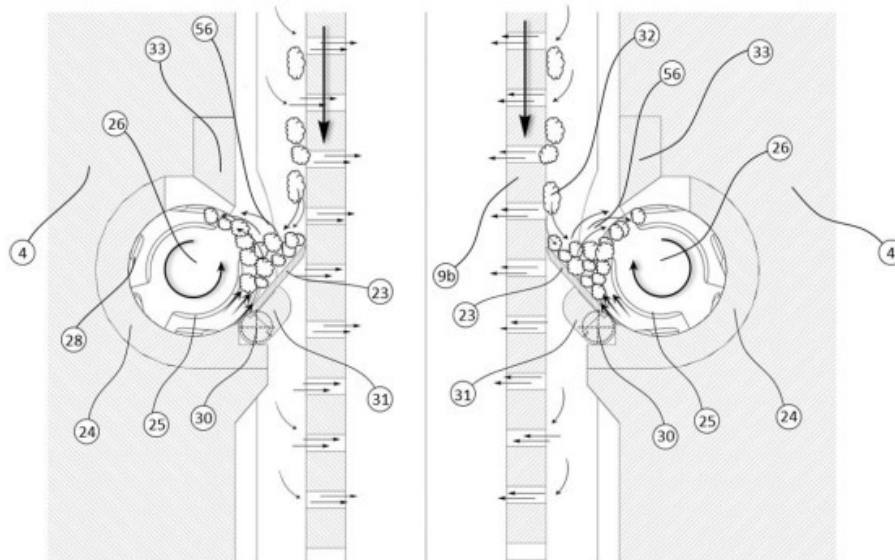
Schnittzeichnung durch die angegriffenen Ausführungsformen
